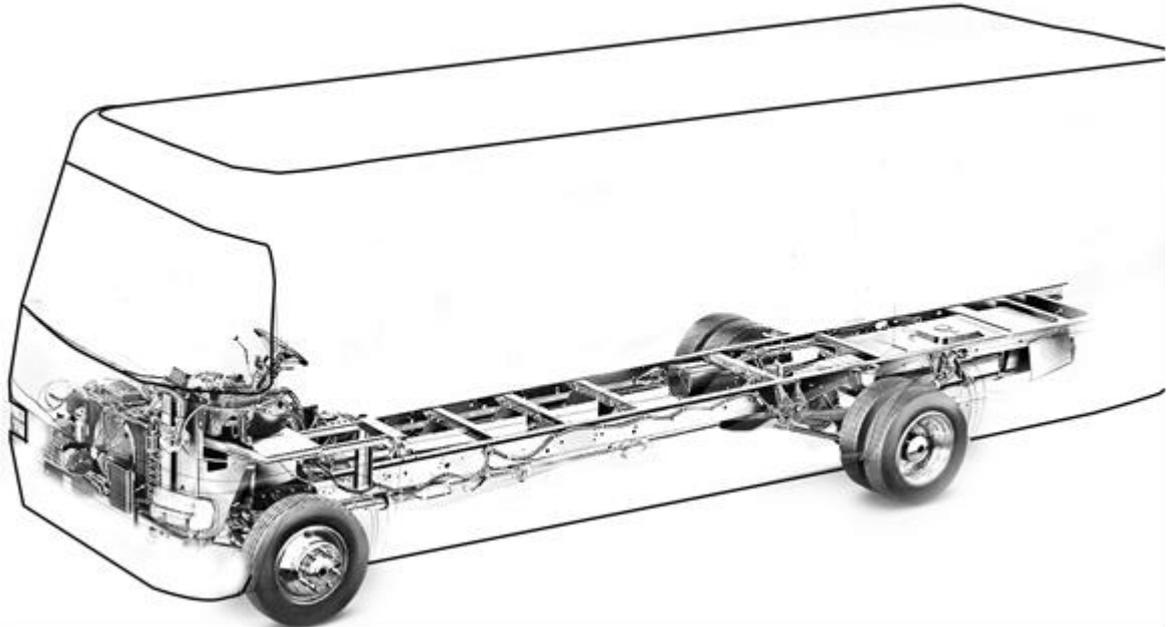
Рама автобуса изготовленного на шасси грузового автомобиля
